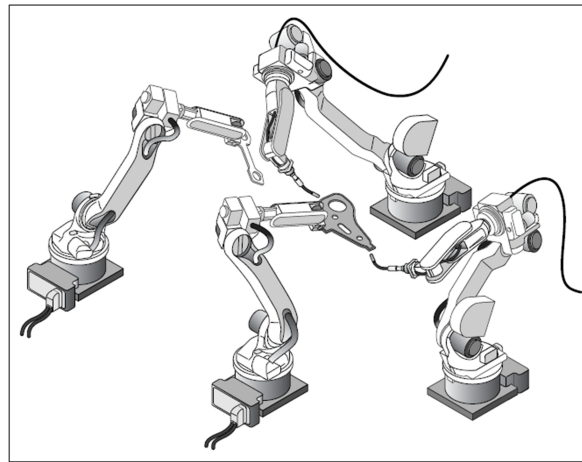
Cooperação em posicionamento e soldagem (YASKAWA, 2007)
